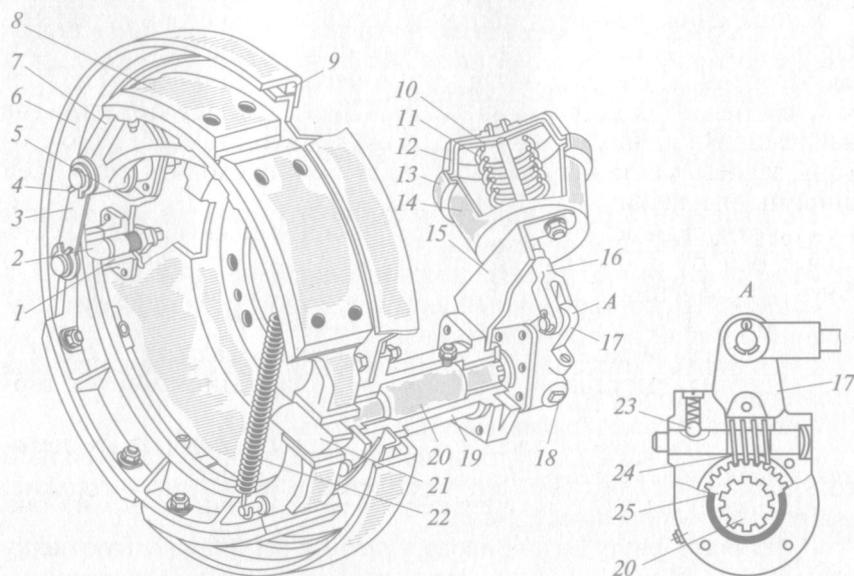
Колесный тормозной механизм автомобиля ЗИЛ-130:
